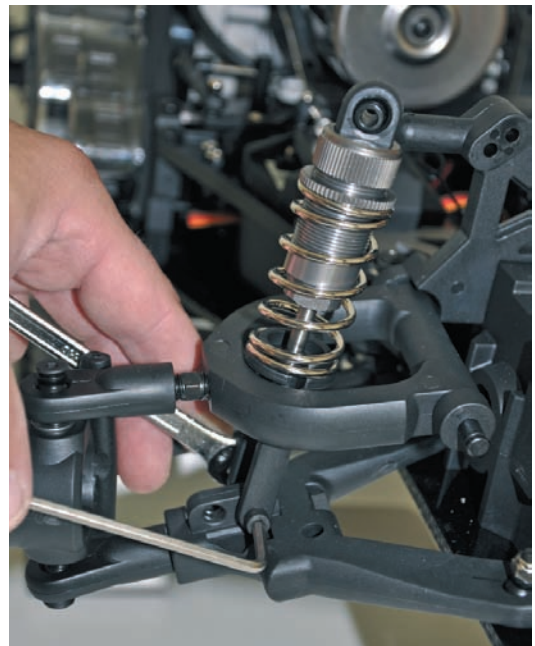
Die Stoßdämpfergabel ist mit einer Schraube und einer Mutter beweglich am unteren Querlenker angeschraubt.
